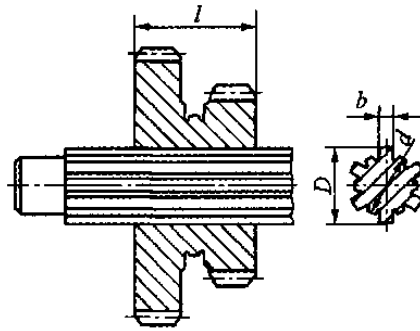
Прямобочное зубчатое соединение
